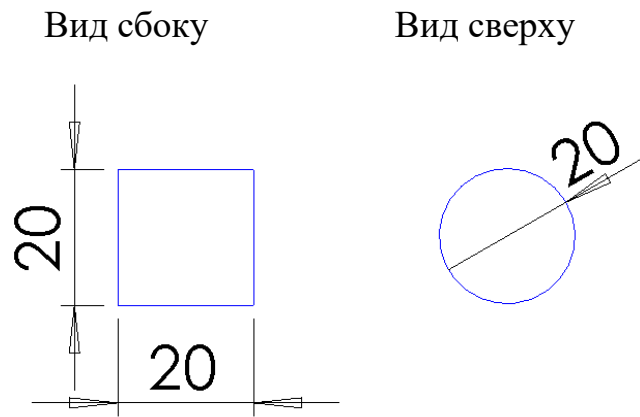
Чертеж образца для проведения испытаний на сжатие
